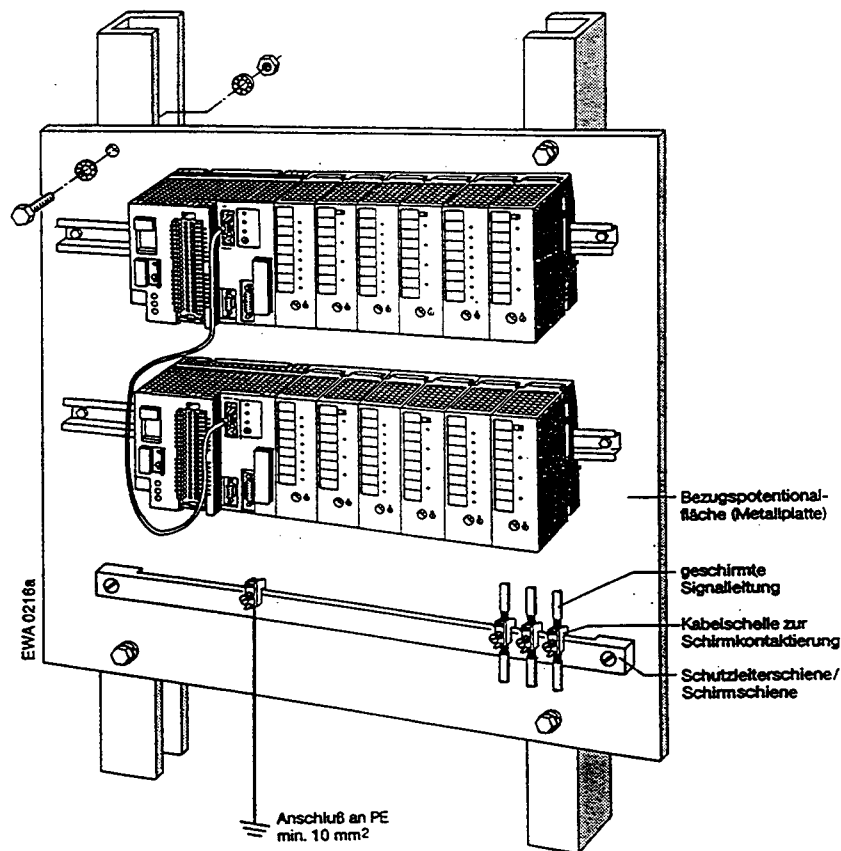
Gerüstmontage eines zweizeiligen Aufbaus mit S5-95F
